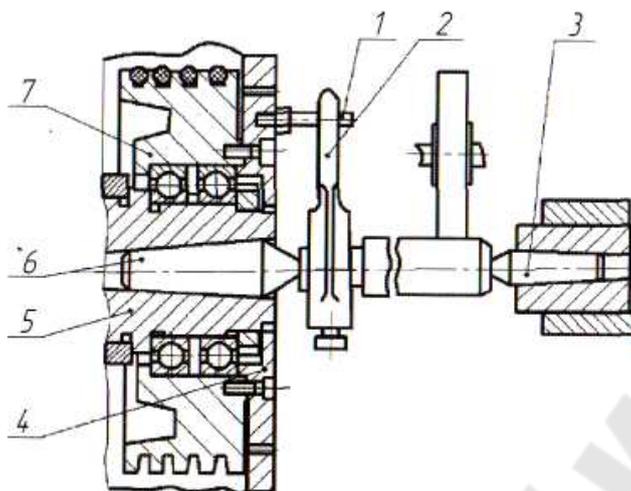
Схема установки заготовки в центрах: 1 – поводковый палец; 2 – хомутик; 3 – задний упорный центр; 4 – поводковый диск (планшайба); 5 – шпиндель передней бабки станка; 6 – передний упорный центр; 7 – шкив
